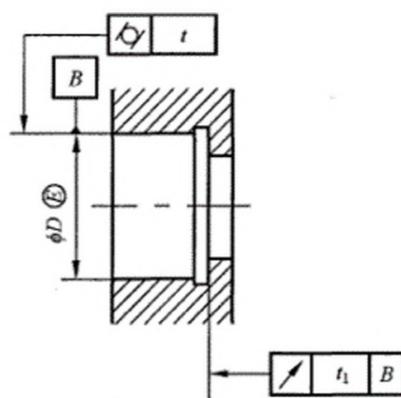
轴承座孔表面的圆柱度公差和孔肩的轴向圆跳动
